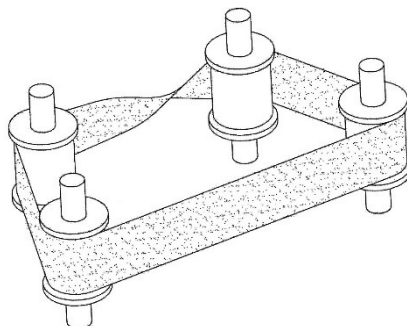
Плоскошліфувальний пристрій (пат. CN104907905A)
